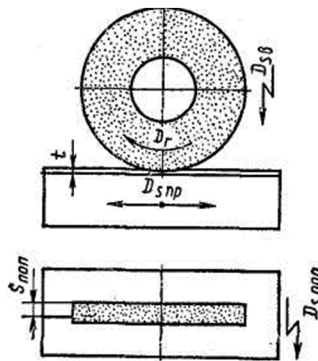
Схема обработки заготовки на плоскошлифовальном
